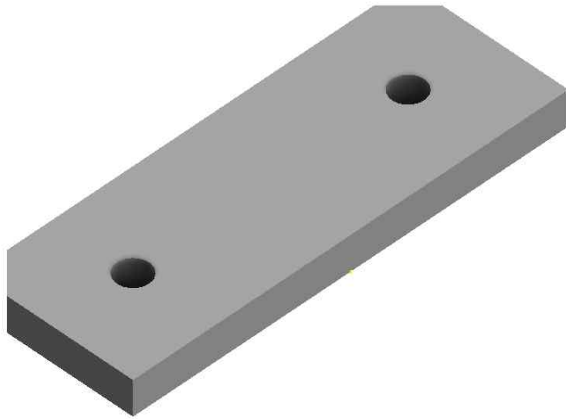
펌프일체형수문 Side Roller 구성품 모델링
